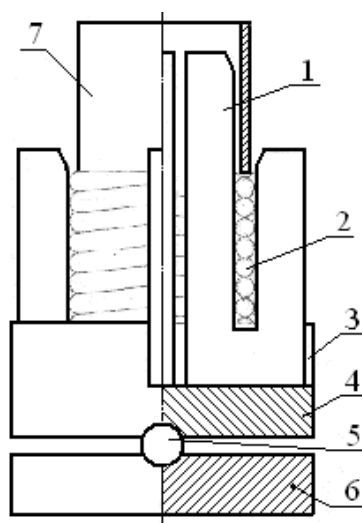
Устройство для заневоливания пружин по а. с. 643684 [95]
